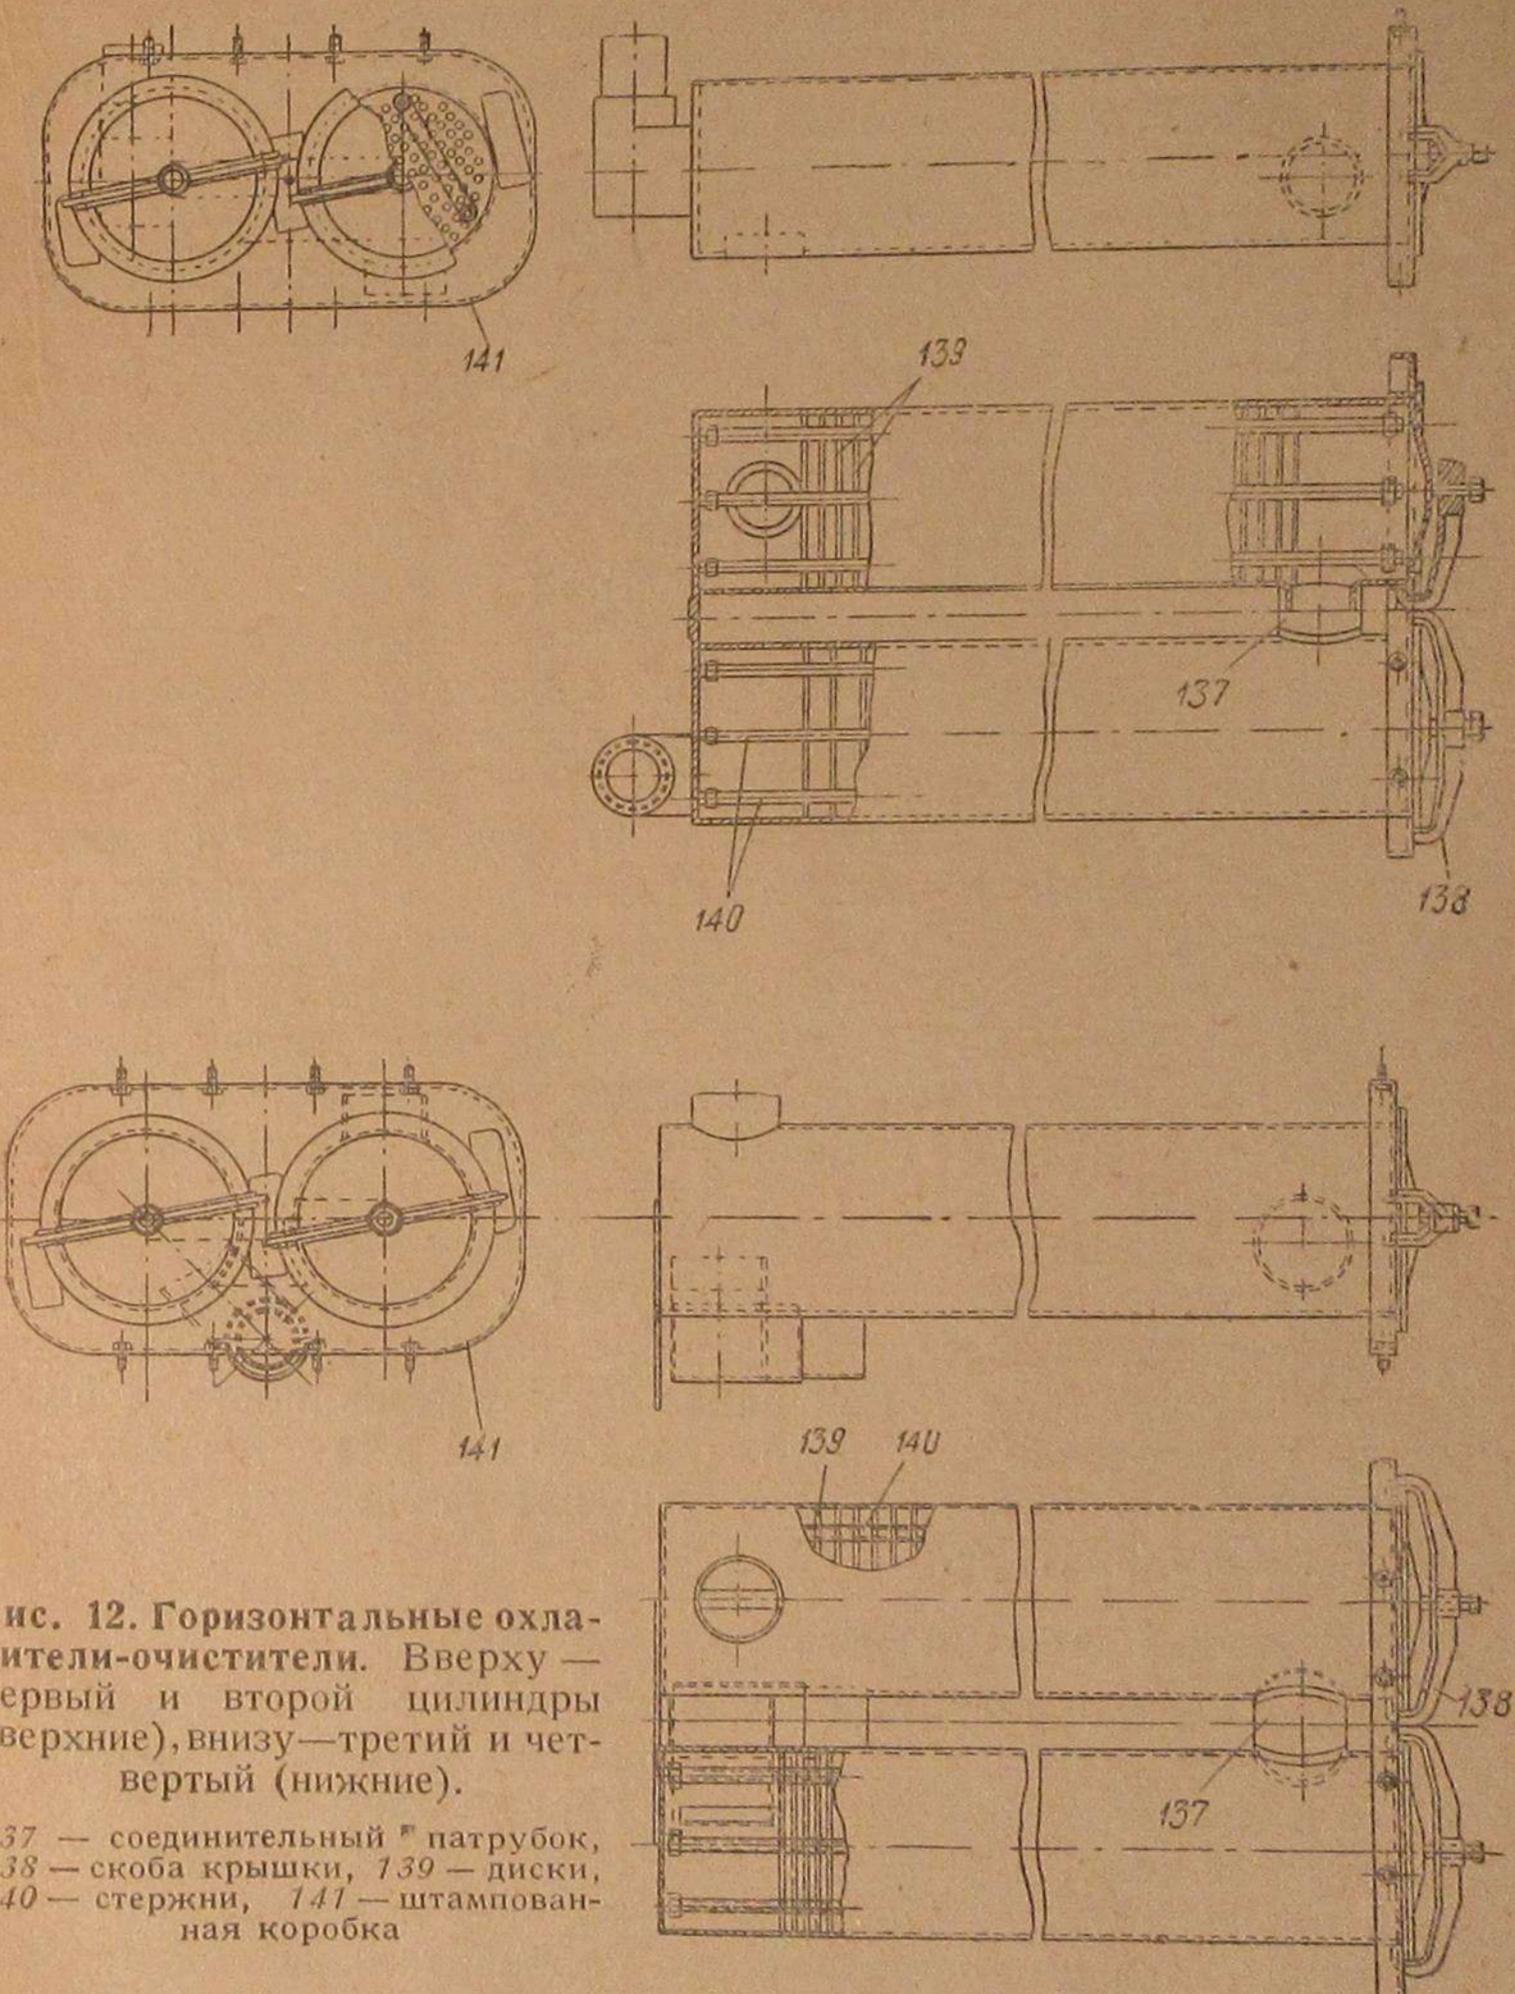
Горизонтальные охладители-очистители. Вверху — первый и второй цилиндры (верхние), внизу — третий и четвертый (нижние).
